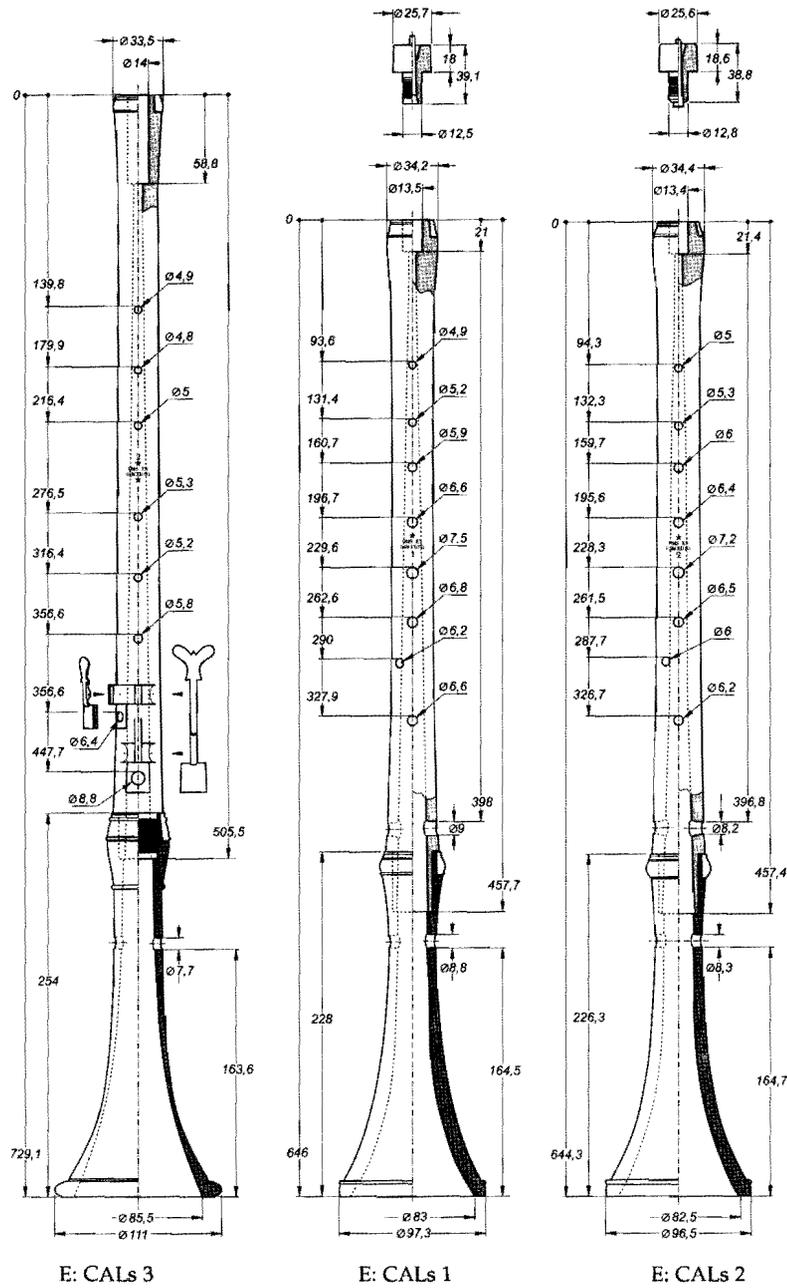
Planos constructivos de las tres chirimías Oms (E: CALs).
